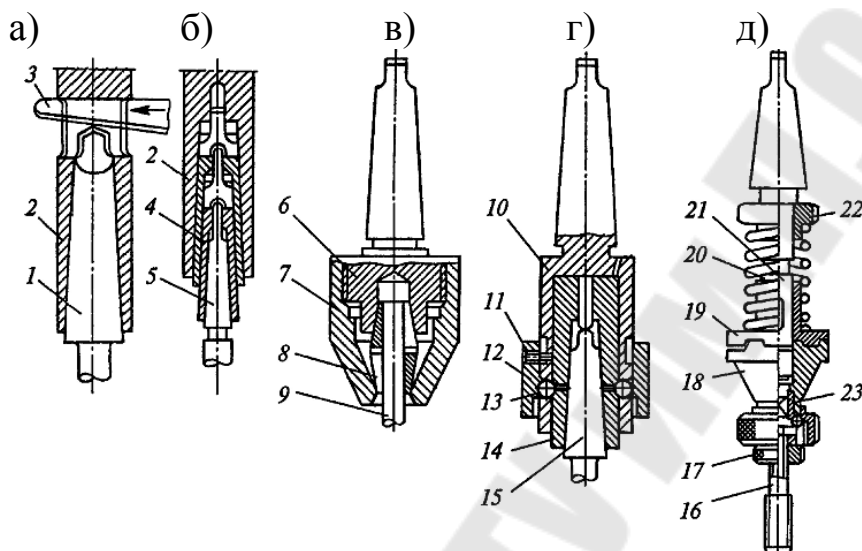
Устройства для закрепления осевого инструмент на сверлильных станках:
